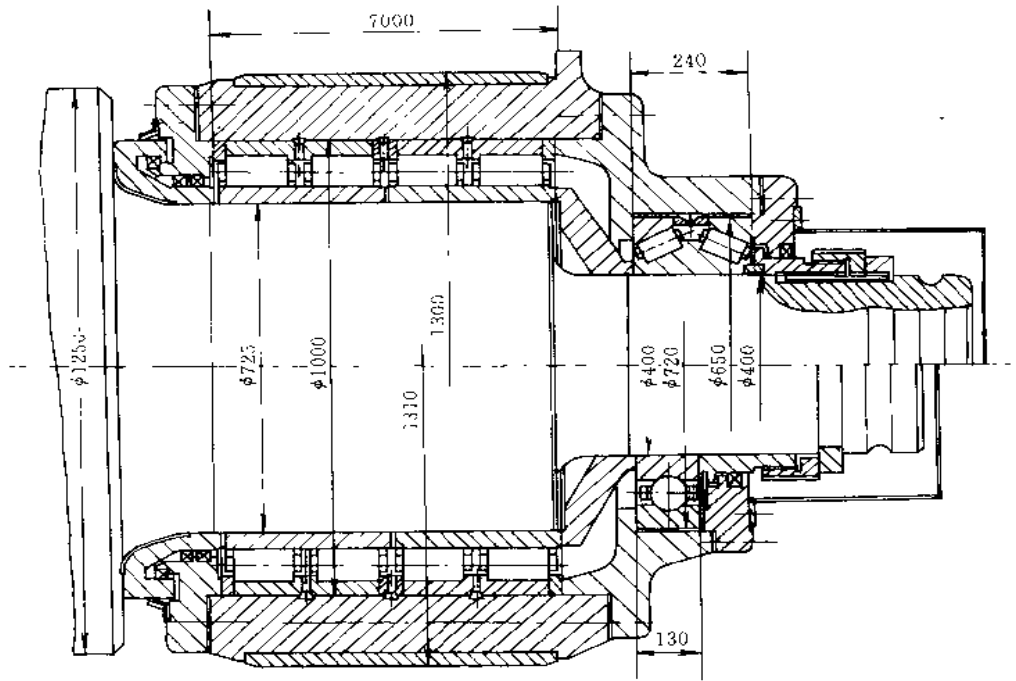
轧辊轴承选用四列圆柱滚子轴承结构
